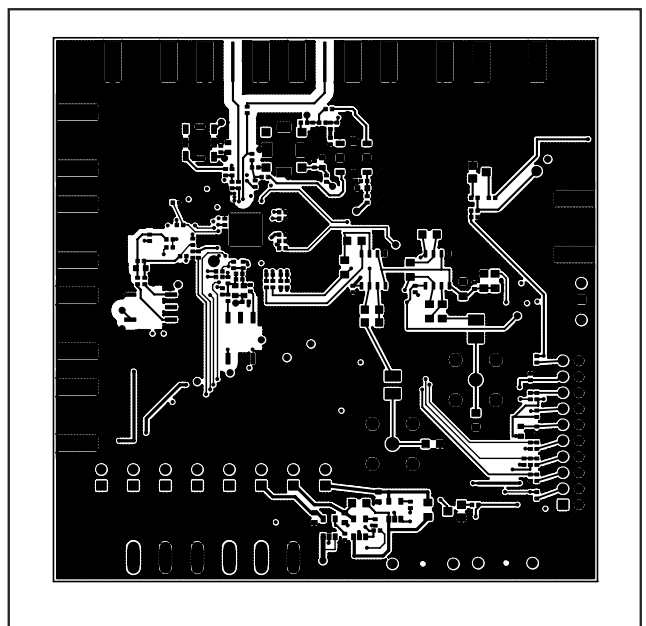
MAX2370评估板PCB布板图——焊接层 (底视图)
